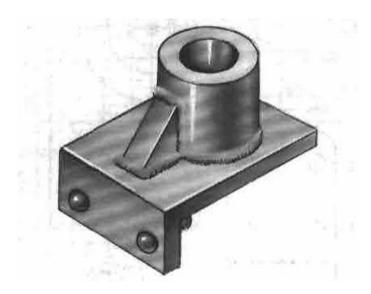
Соединение деталей, выполненное при помощи сварки
